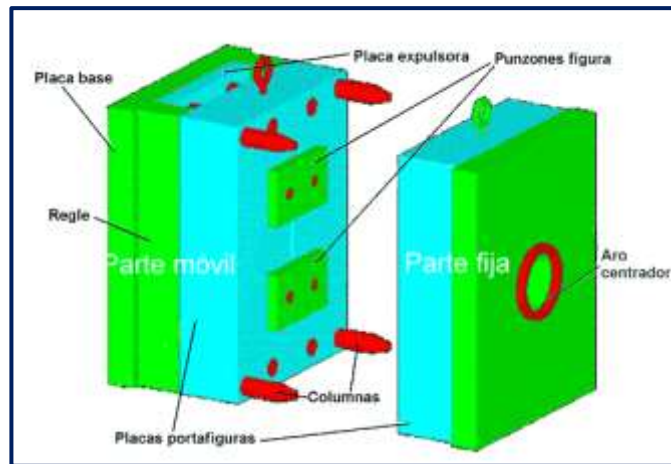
Partes de un molde en una máquina de inyección por moldeo.
